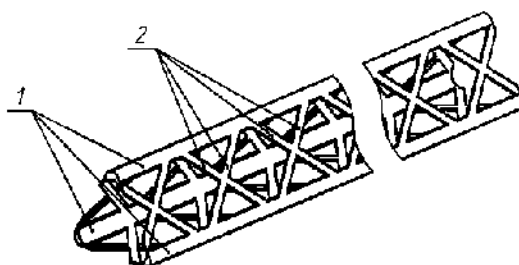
Конструкция изогридной трубы треугольного сечения
